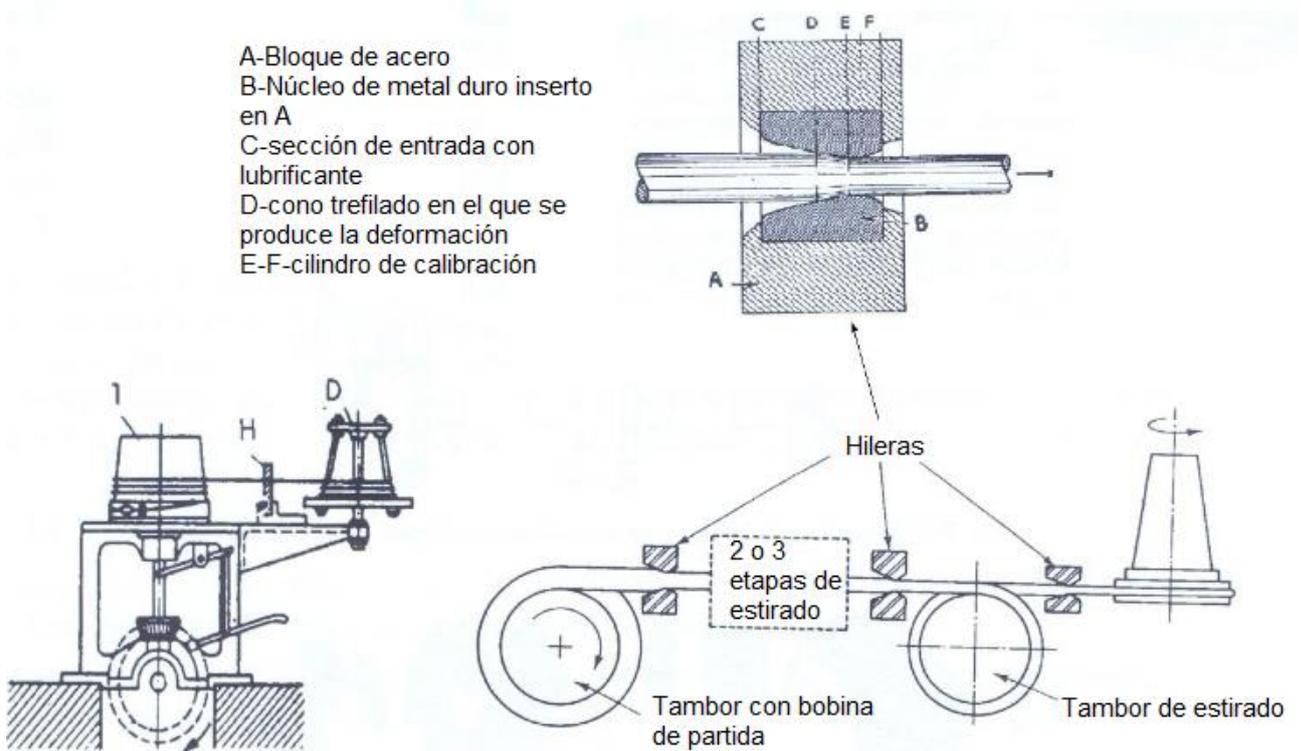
Esquema de la obtención de cables mediante trefilado.
